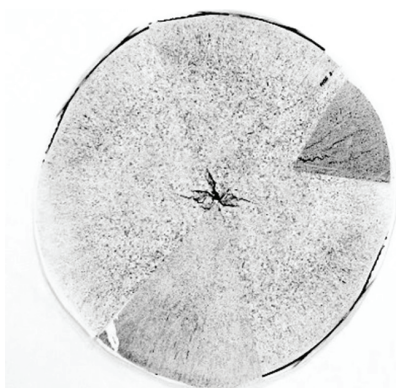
Осевая трещина в непрерывно-литой круглой заготовке  $\varnothing 430$  мм из колесной стали
